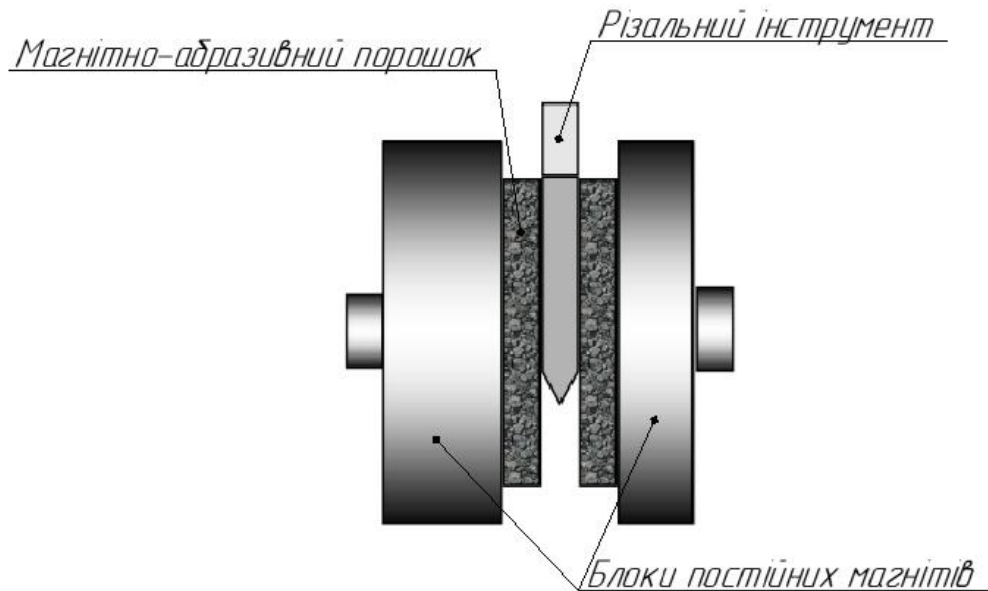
Схема пакетного полірування за допомогою магнітного поля [65]
